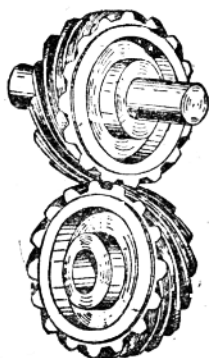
两轴成 90° 时用斜齿圆柱齿轮传动。
